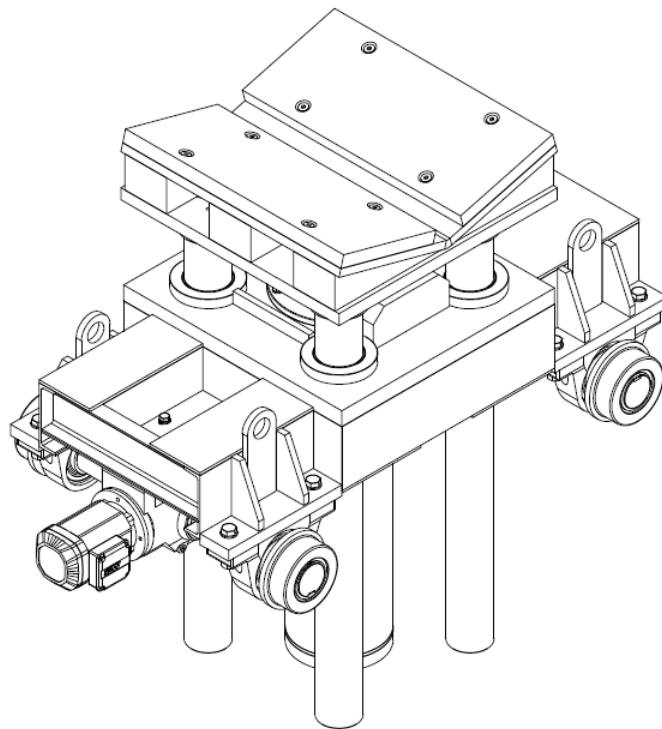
Croqui do conjunto elevador de bobina da máquina LCT.
